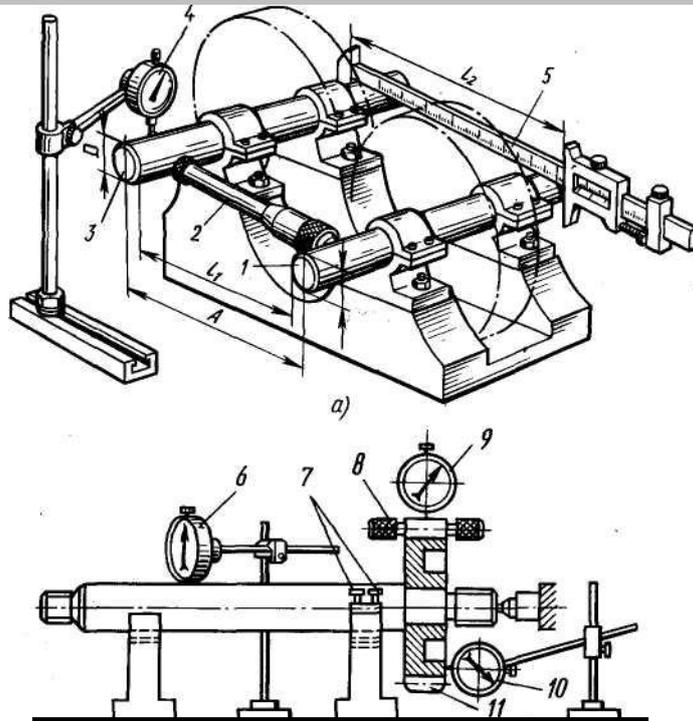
Схемы проверки расположения отверстий в корпусе редуктора и биения зубчатых колес: 1, 3, 8 — калибры, 2 — нутромер микрометрический. 4, 6, 9, 10 — индикаторы, 5 — штангенциркуль, 7 — винты, 11 — проверяемое зубчатое колесо.
